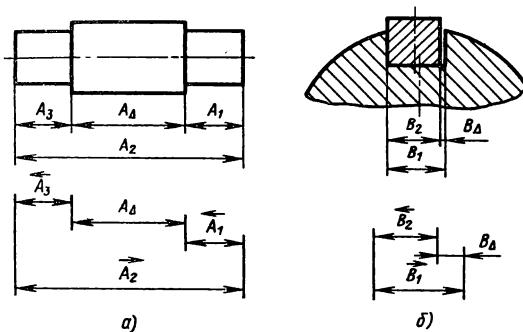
Подетальная (а) и сборочная (б) размерные цепи
